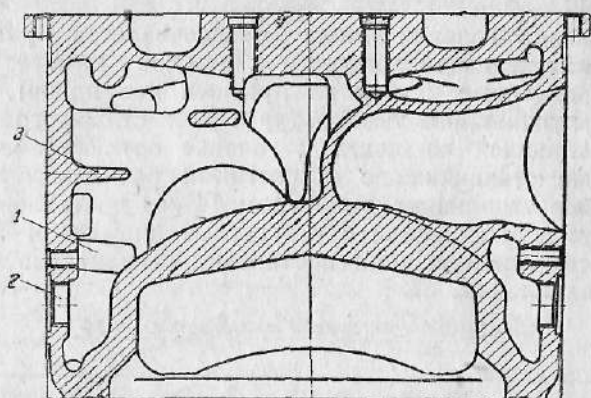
Схема постановки трубок перепуска воды из рубашек цилиндров в головки блоков.
